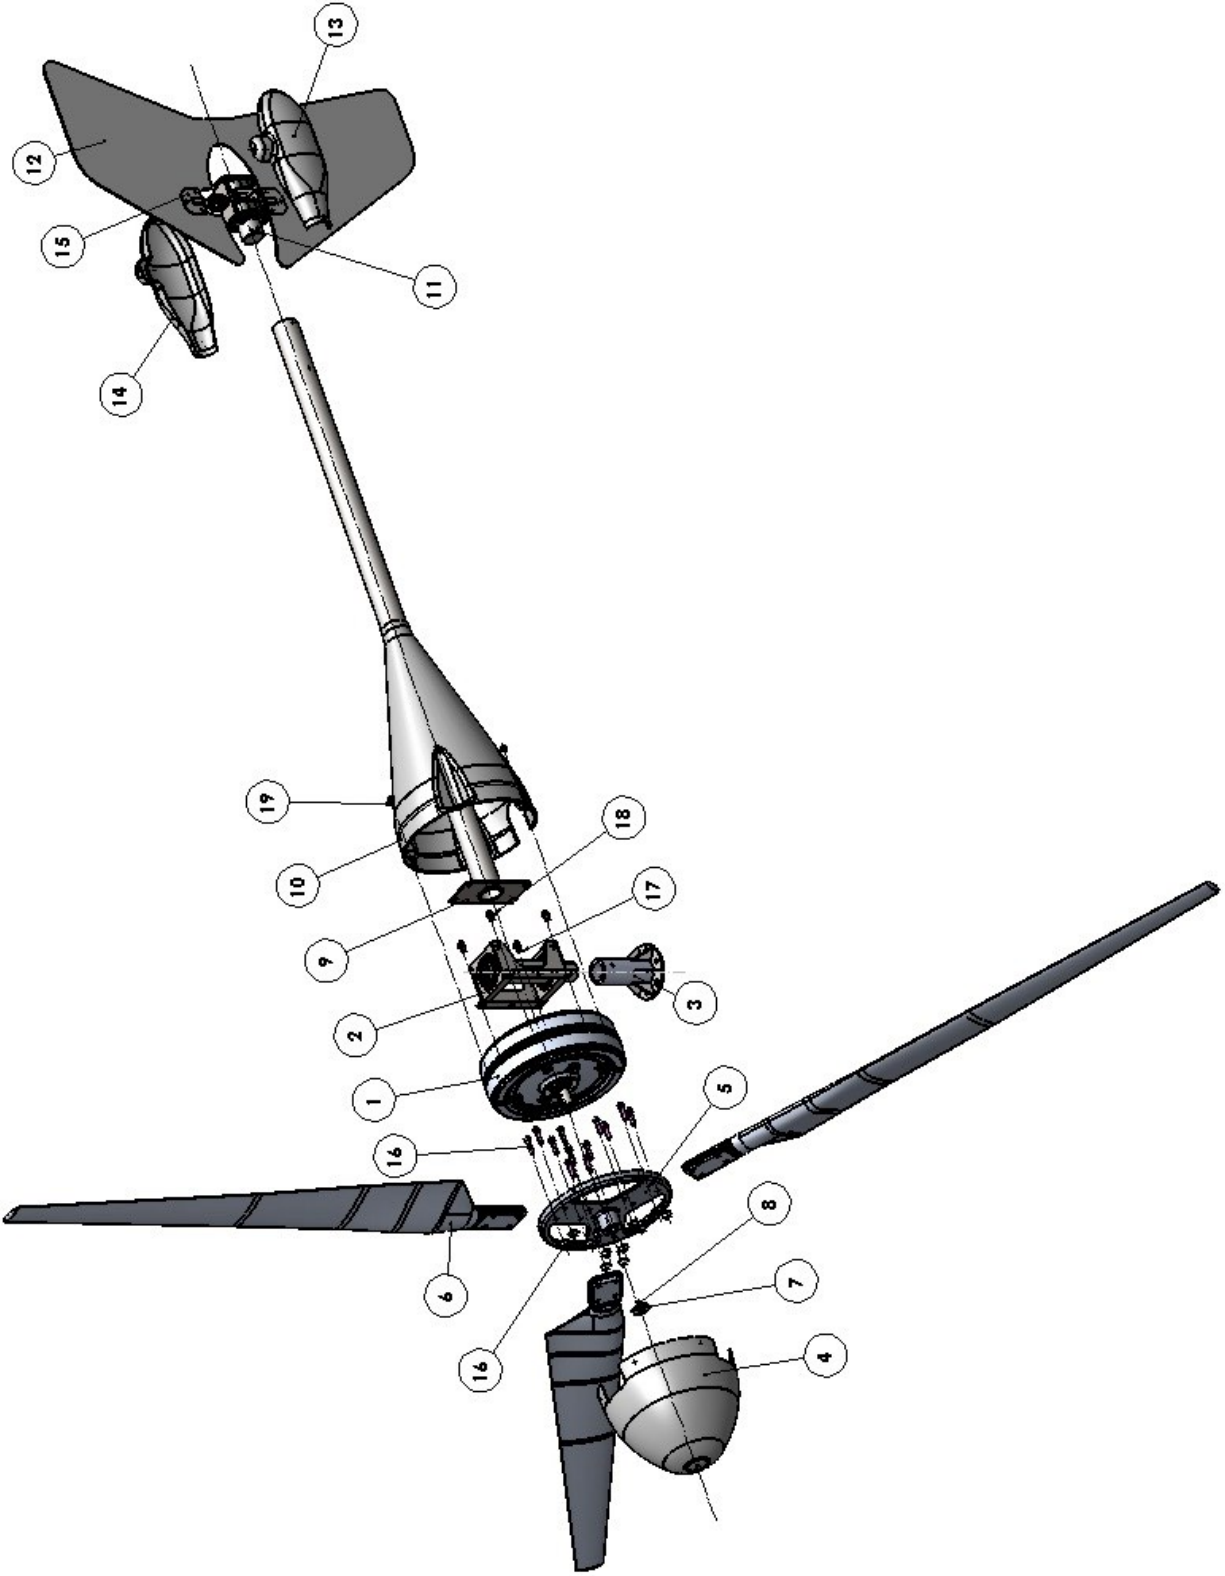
Turbina eoliana cu ax orizontal - Vedere explodată a ansamblului.
